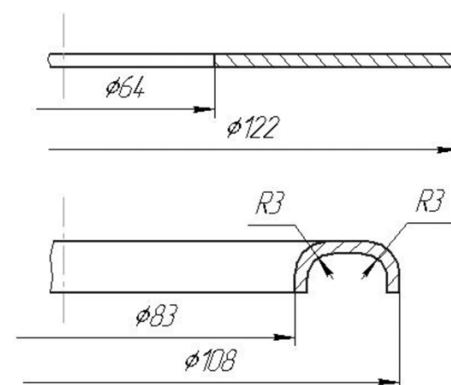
Геометрические размеры заготовки и кольцевого образца
